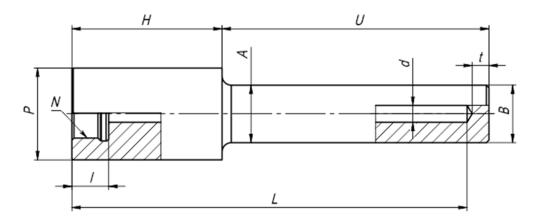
Гильза под приварку через адаптер (Socket Weld), цельноточёная, прямая, под неподвижный штуцер.
